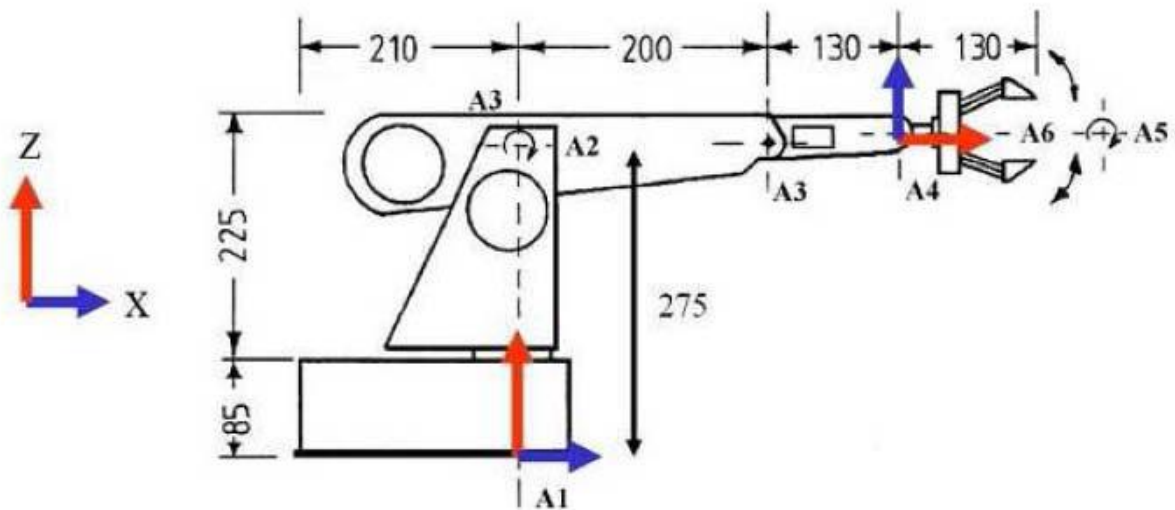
Les dimensions du robot ROB3 (vue de face).
